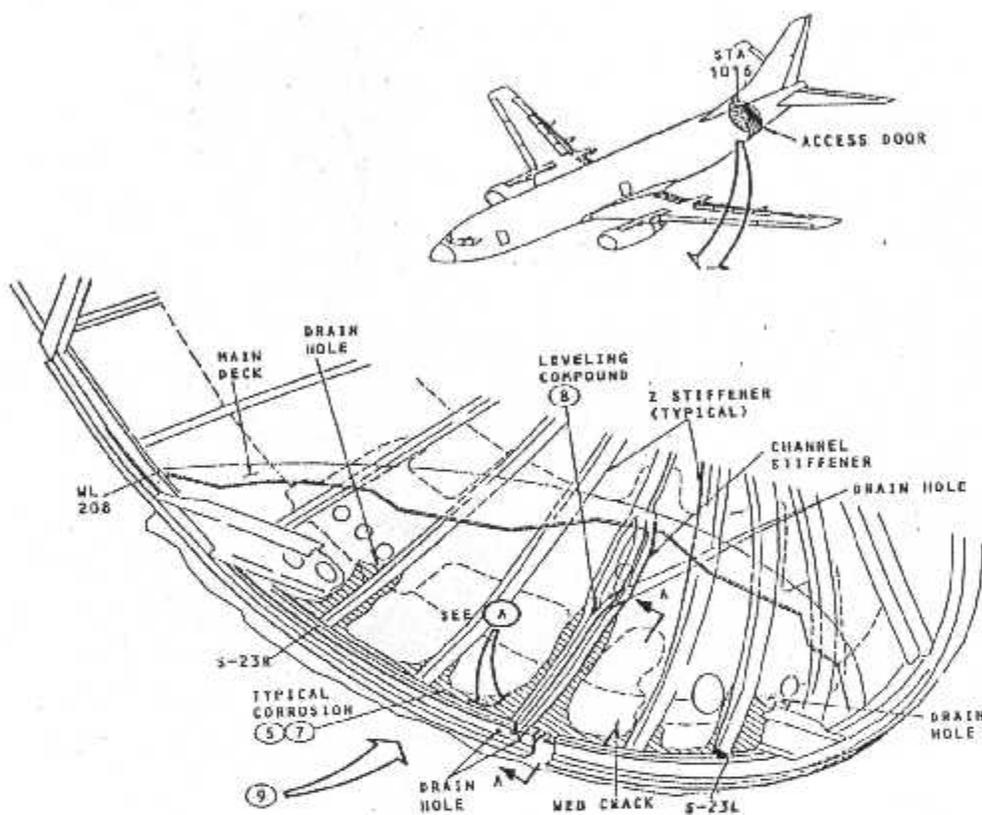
vue d'ensemble de la C.E.P (coté bas)
